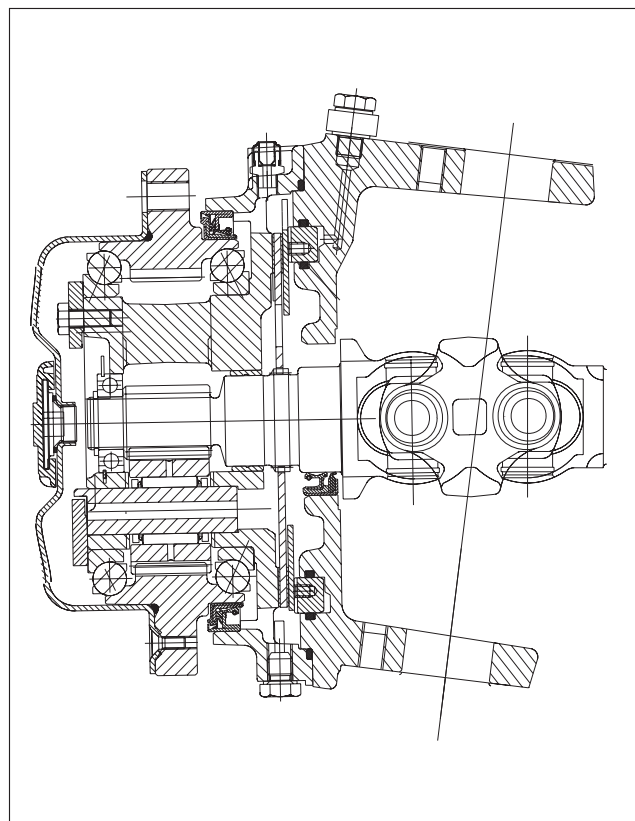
Montage de la bague d'étanchéité du piston de compression des freins avant.
